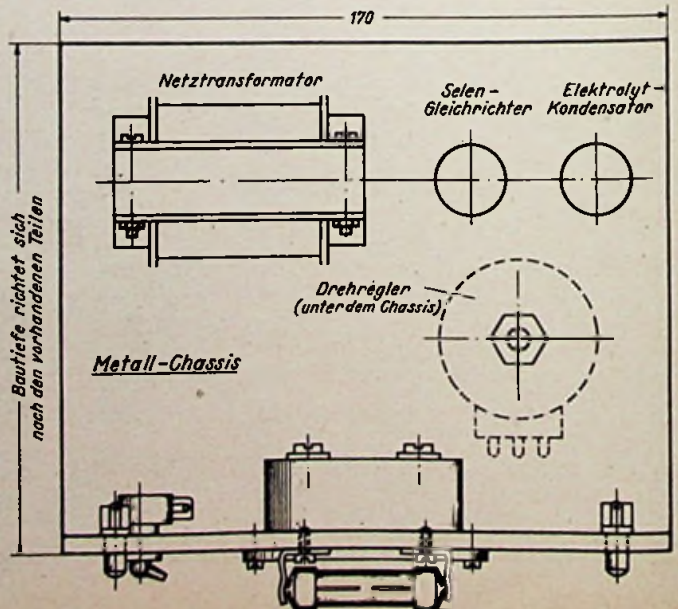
Frontplatte und Chassisaufsicht des Prüfgerätes. Zweckmäßig wird zum Aufbau ein vorhandenes Gehäuse mit etwa gleich großen Abmessungen verwendet
